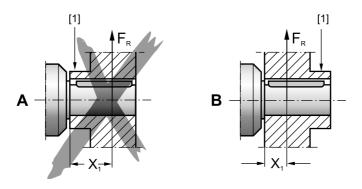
Disposição de montagem correcta de uma polia ou roda dentada
